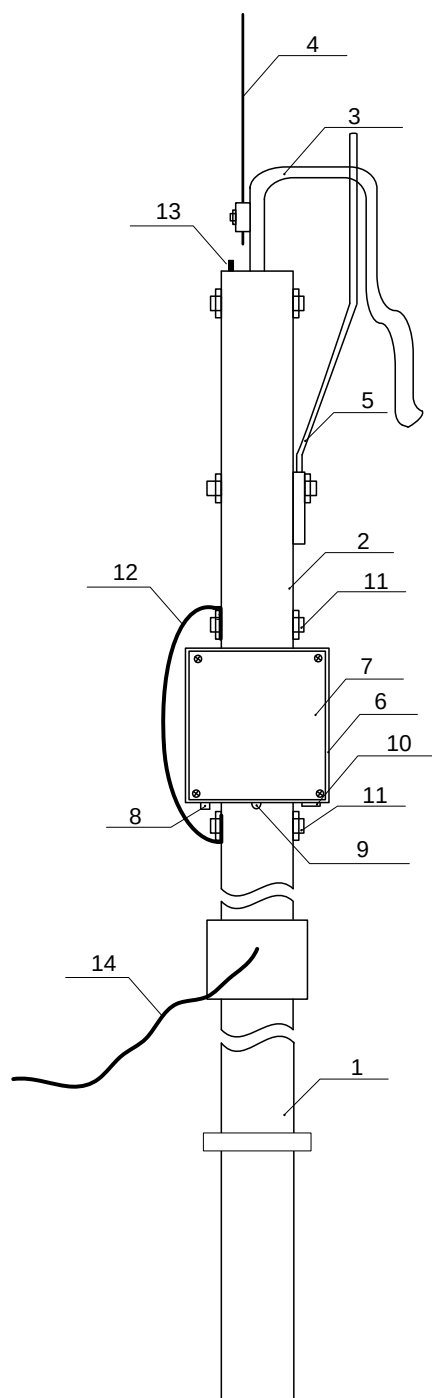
Чертеж корпуса контролирующего устройства для монтажа в разрез верхней токопроводящей части переносного заземляющего устройства
